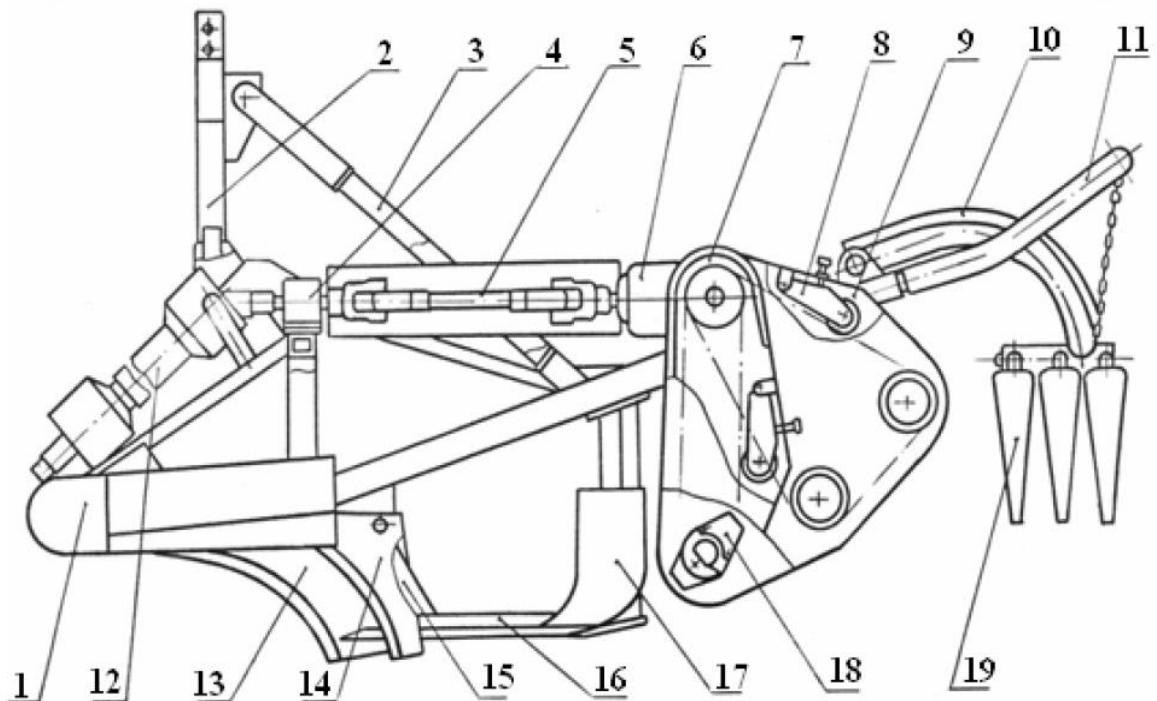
Машина для фрезерования почв: 1-рама; 2-навесное устройство; 3-наклонная тяга; 4-промежуточная опора; 5-промежуточный карданный вал; 6-редуктор; 7-левый картер; 8-натяжное устройство; 9-правый картер; 10-отражатель; 11-заднее ограждение; 12-основной карданный вал; 13-средний нож; 14-боковой нож; 15-средняя стойка; 16-горизонтальный нож; 17-отвал; 18-ротор; 19-скат
